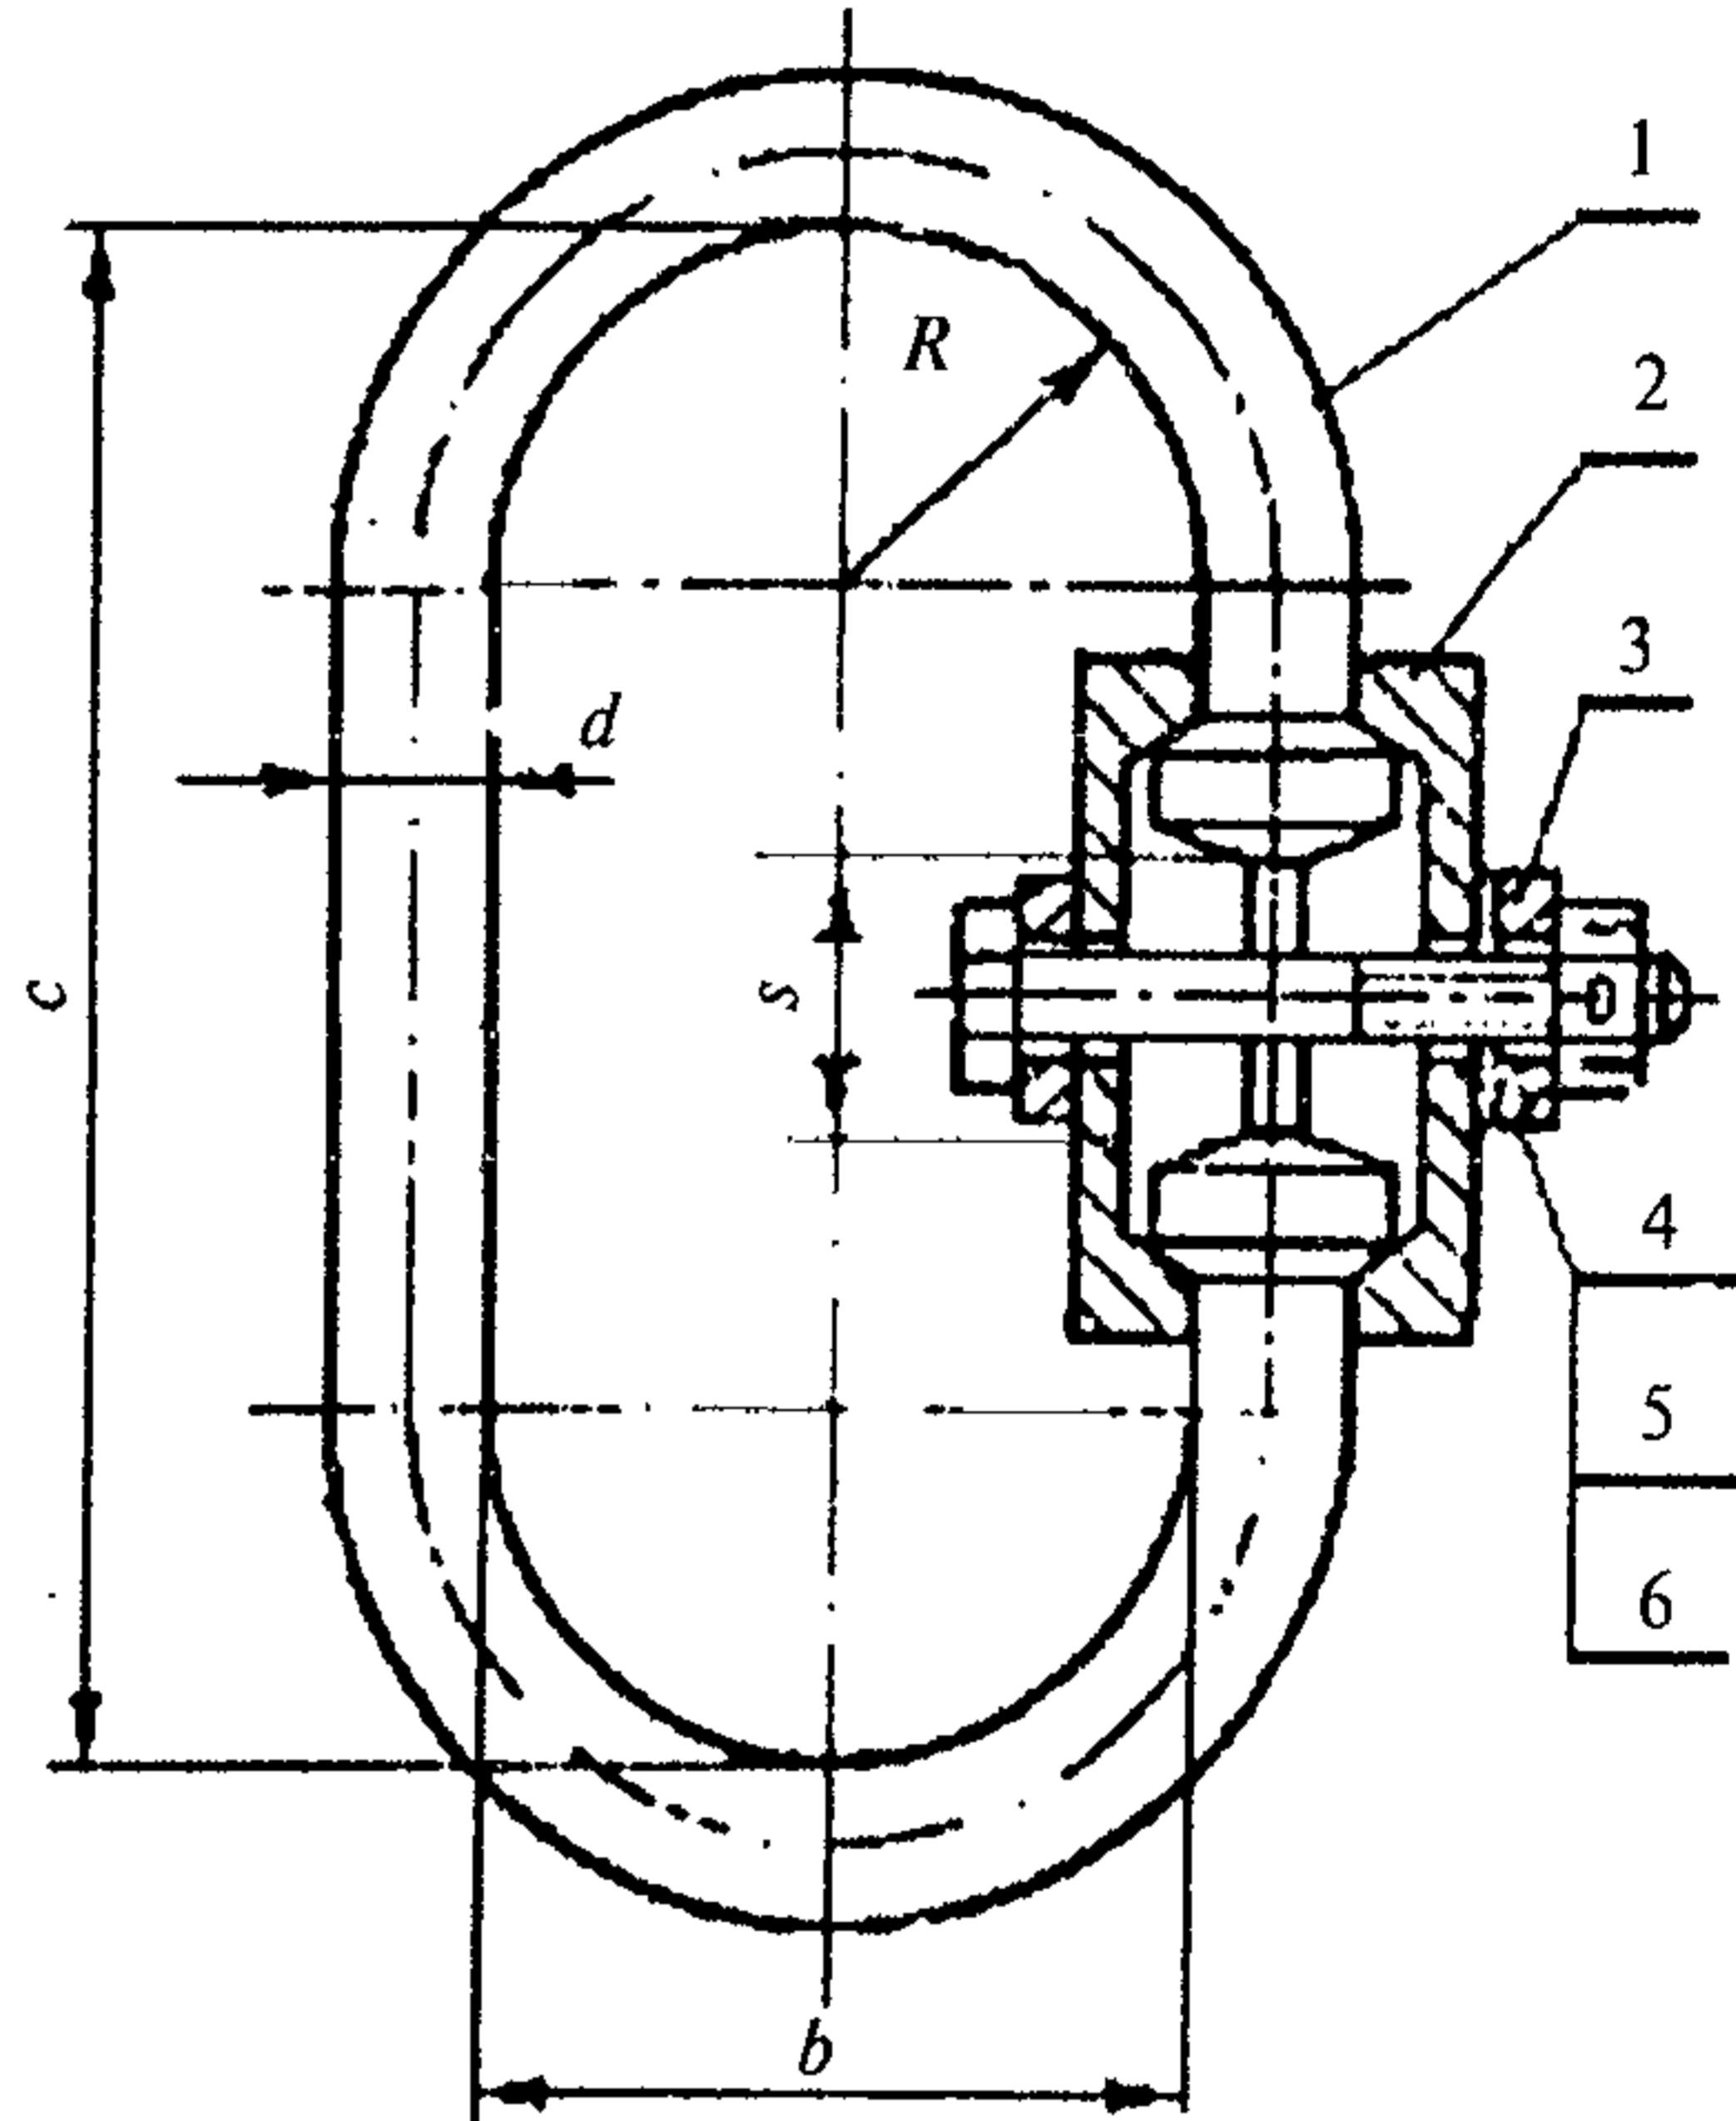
Звено Ров с допускаемой нагрузкой до 2 тс
